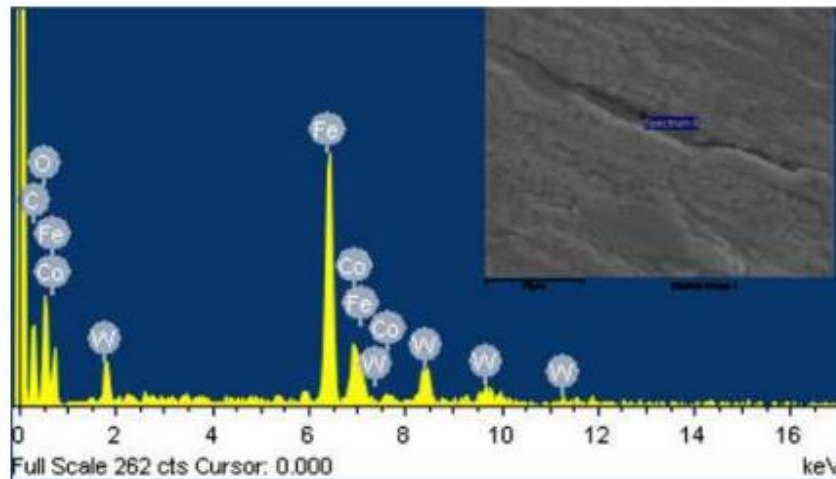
Результати дослідження поверхні інструменту з наявністю дифузійного механізму зношування інструменту при торцевому фрезеруванні AISI 1045
